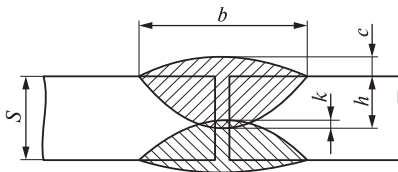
Схема двустороннего стыкового сварного соединения
